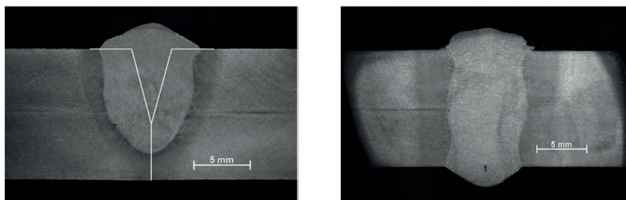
Einseitig ausgeführte Schweißnähte; links: ohne, rechts: mit Durchschweißung
